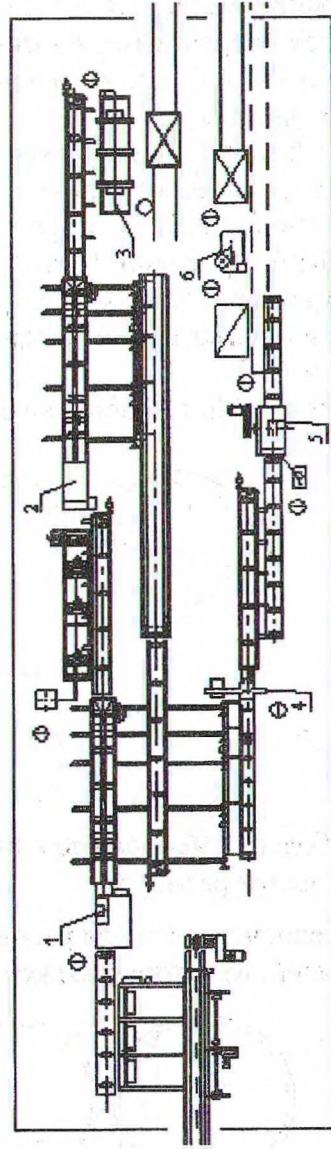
Технологическая схема лесопильного цеха: 1 – круглопильный станок для раскря бревен; 2 – многопильный станок для раскря брусев; 3 – трехпильная торцовочная установка проходного типа; 4 – торцовочный станок; 5 – двухпильный обрезной станок; 6 – станок для раскря горбылей
